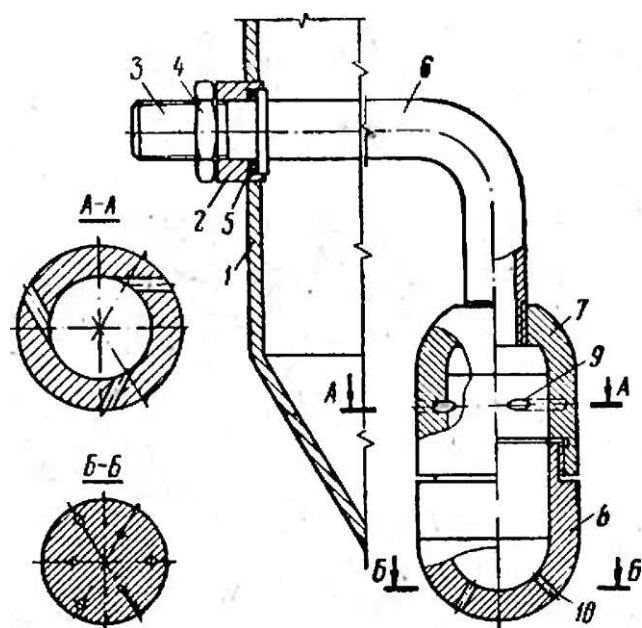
Неподвижный аэратор камерного пневматического зарядчика КПЗП-2:
